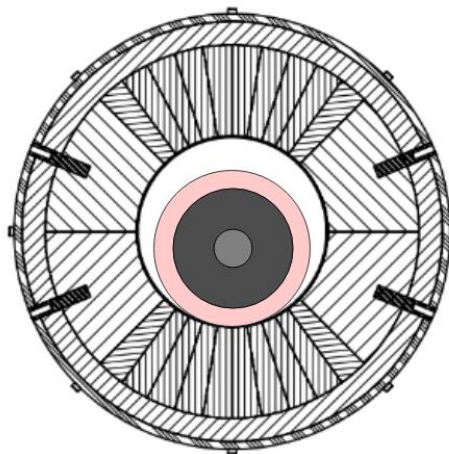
Representação esquemática e fora de escala do conjunto rotor e estator.
